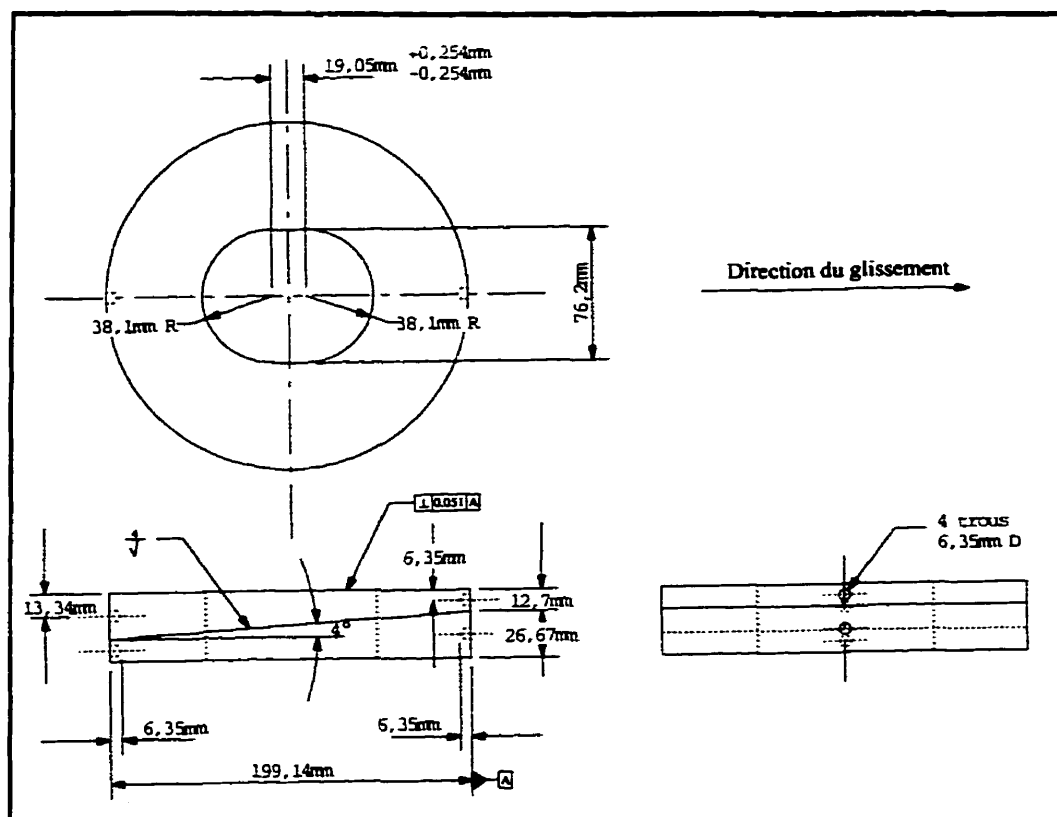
Schéma des rondelles de pré-tension à plan incliné
